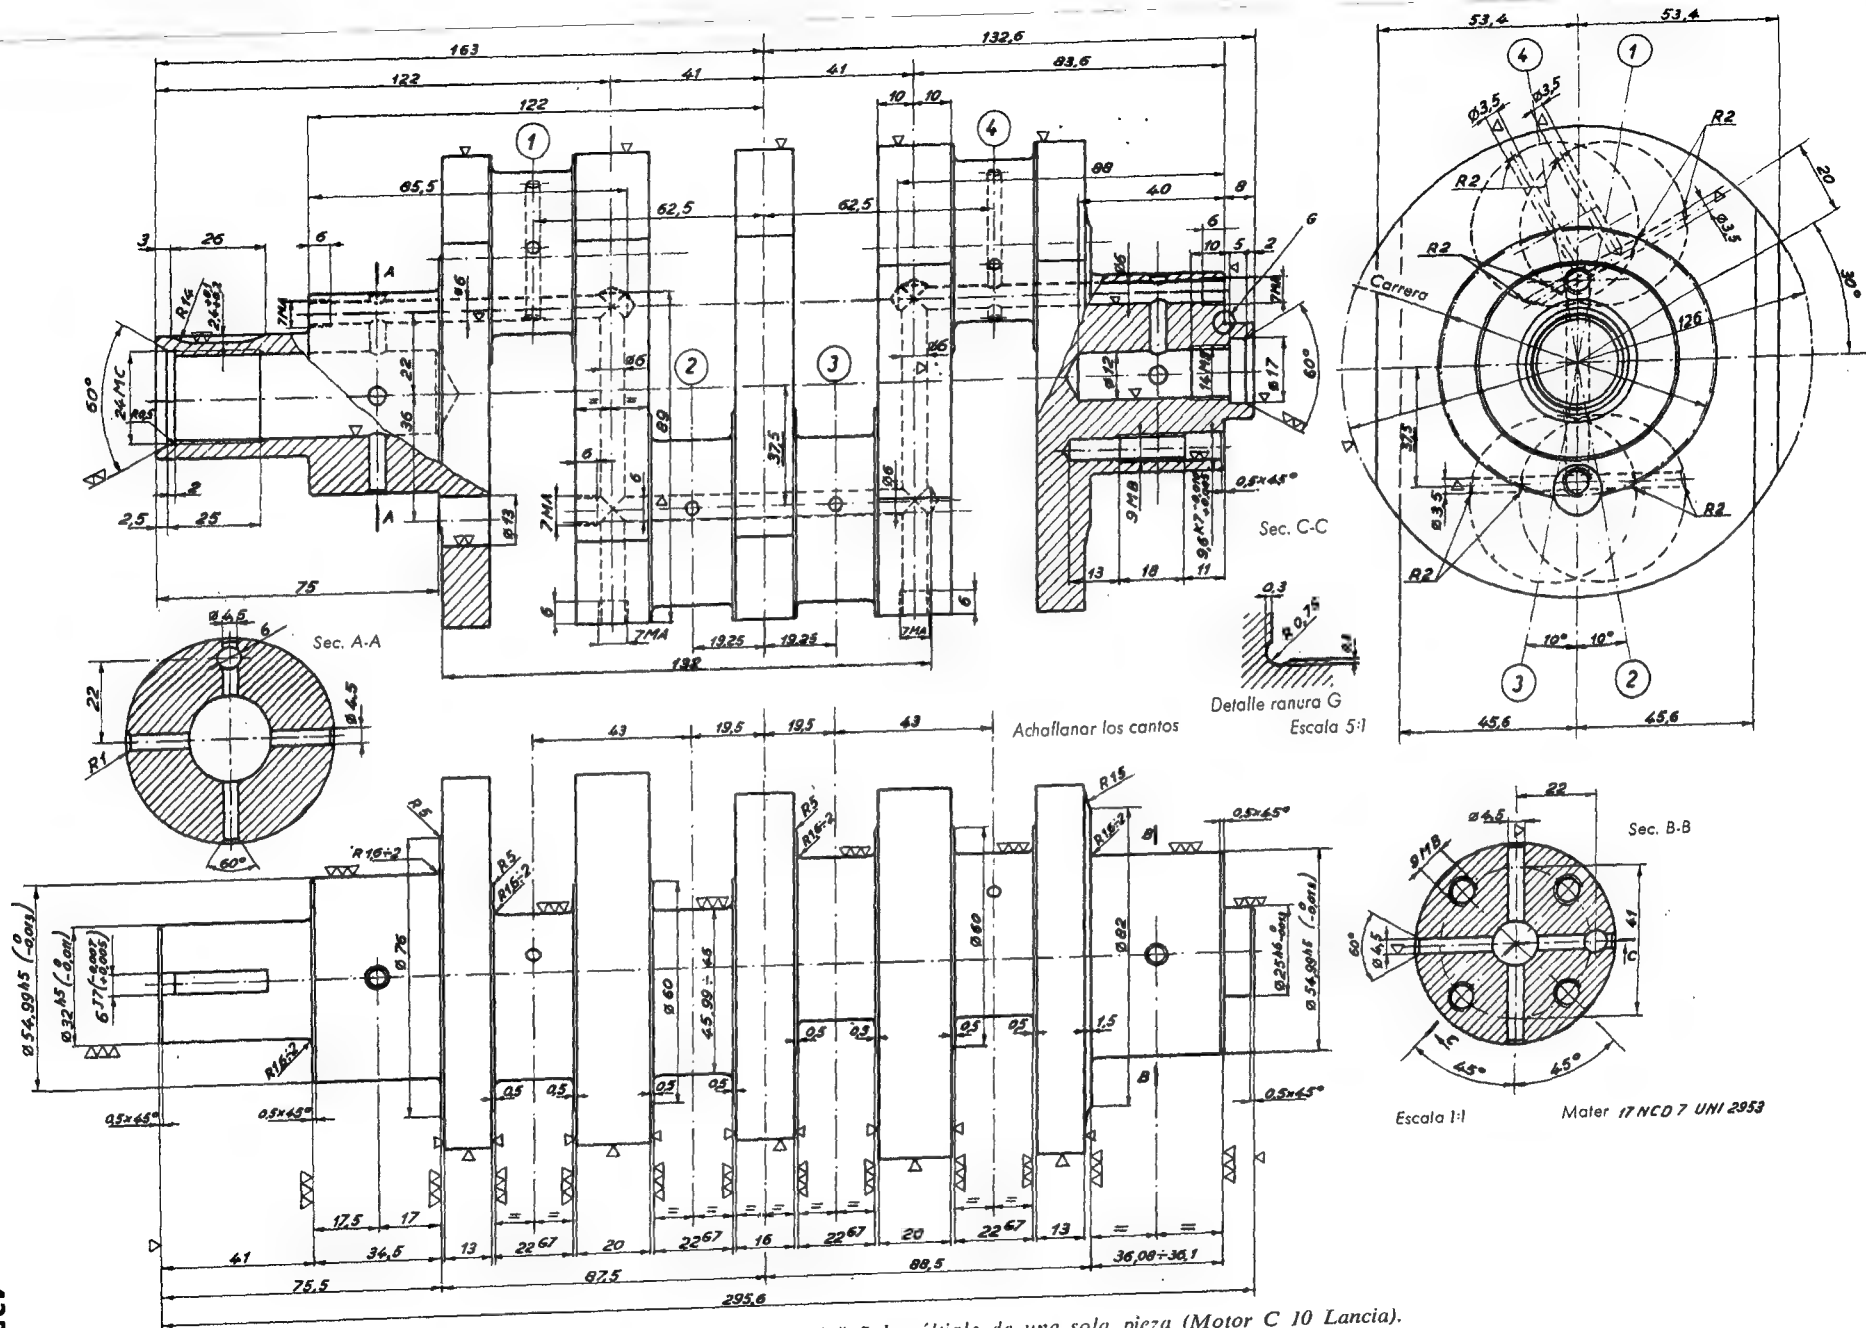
Arbol acodado o cigüeñal múltiple de una sola pieza (Motor C 10 Lancia).
